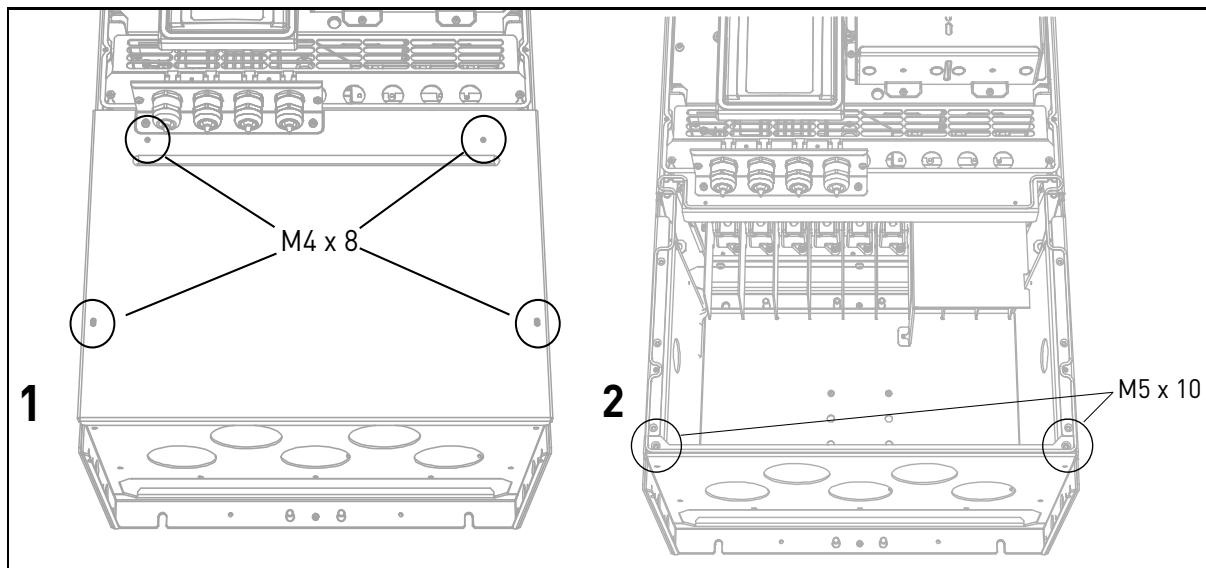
Removendo a tampa do cabo e a placa de fixação do cabo (MR9).
